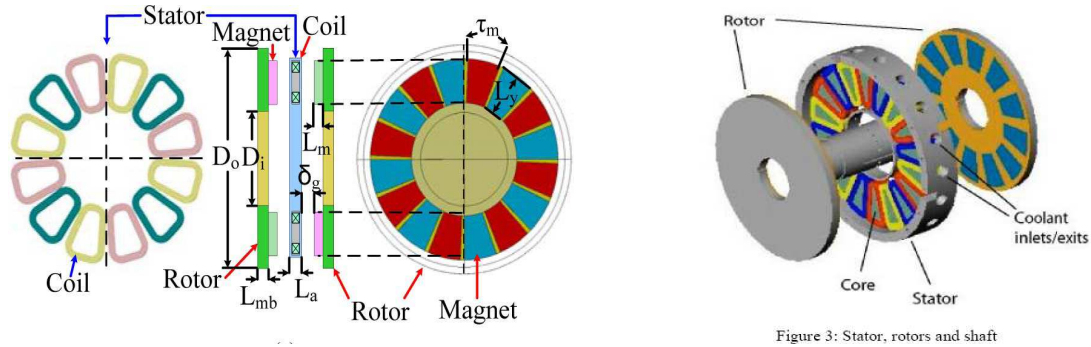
Machine à flux axial à bobinage sur dents 1 stator / 2 rotors.
